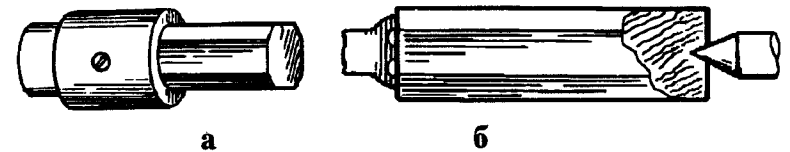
Крепление детали: а — в патроне винтом; б — трезубцем с поджатием центром задней бабки
